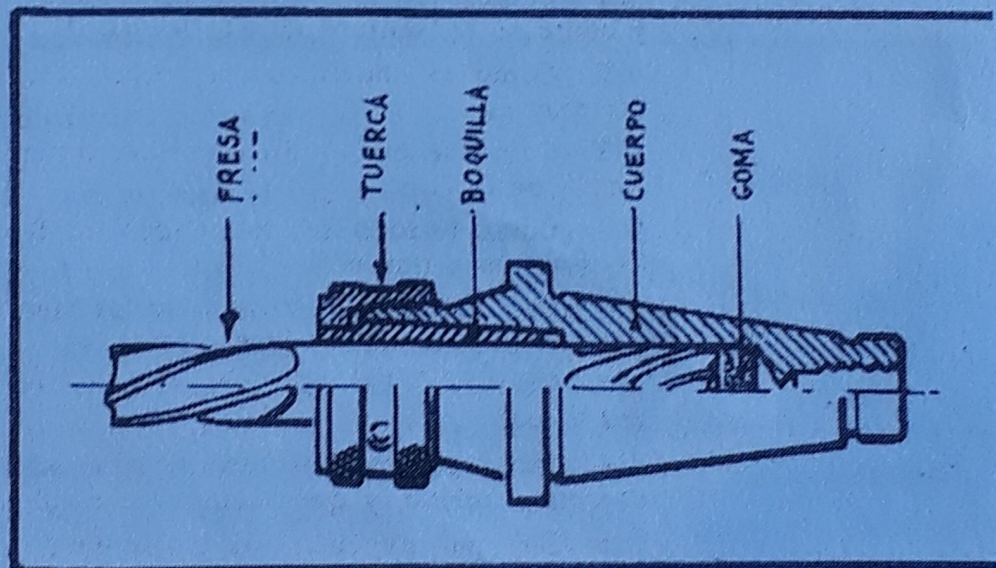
/4. — Pinza para el montaje de una fresa doble de vástago cilíndrico.
